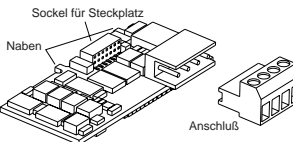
Entfernen Sie den Steckverbinder, bevor Sie das Eingang-1-Modul installieren.
